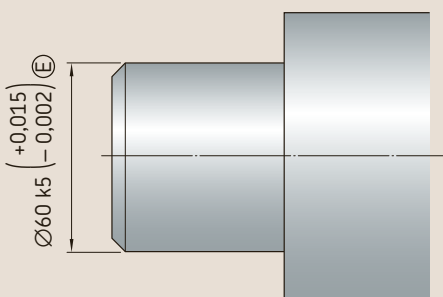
Sistema di tolleranze per l'albero: Estremità dell'albero con dimensione e tolleranza del diametro.
